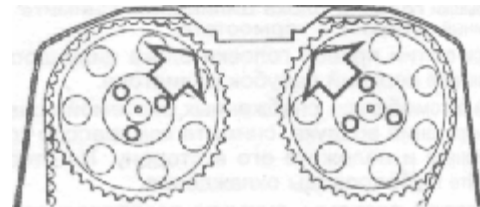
Проверка по установочным меткам — Двигатель B6304F
